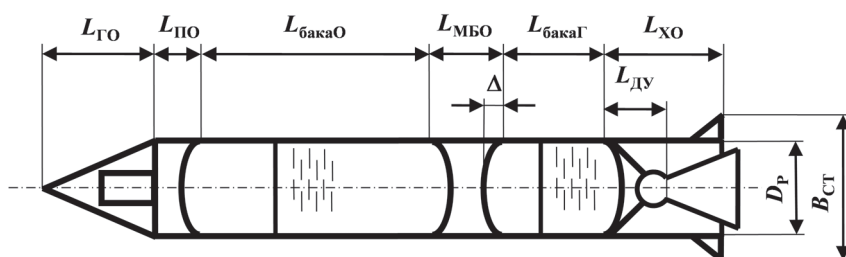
Конструктивно-компоновочная схема одноступенчатой ракеты с обозначением основных геометрических размеров
